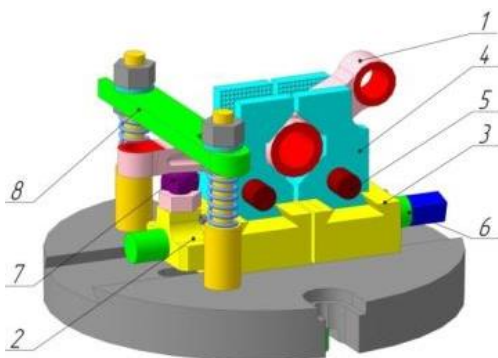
Переналагоджуваний установлювально-затискний модуль для обробки деталей типу важелів
